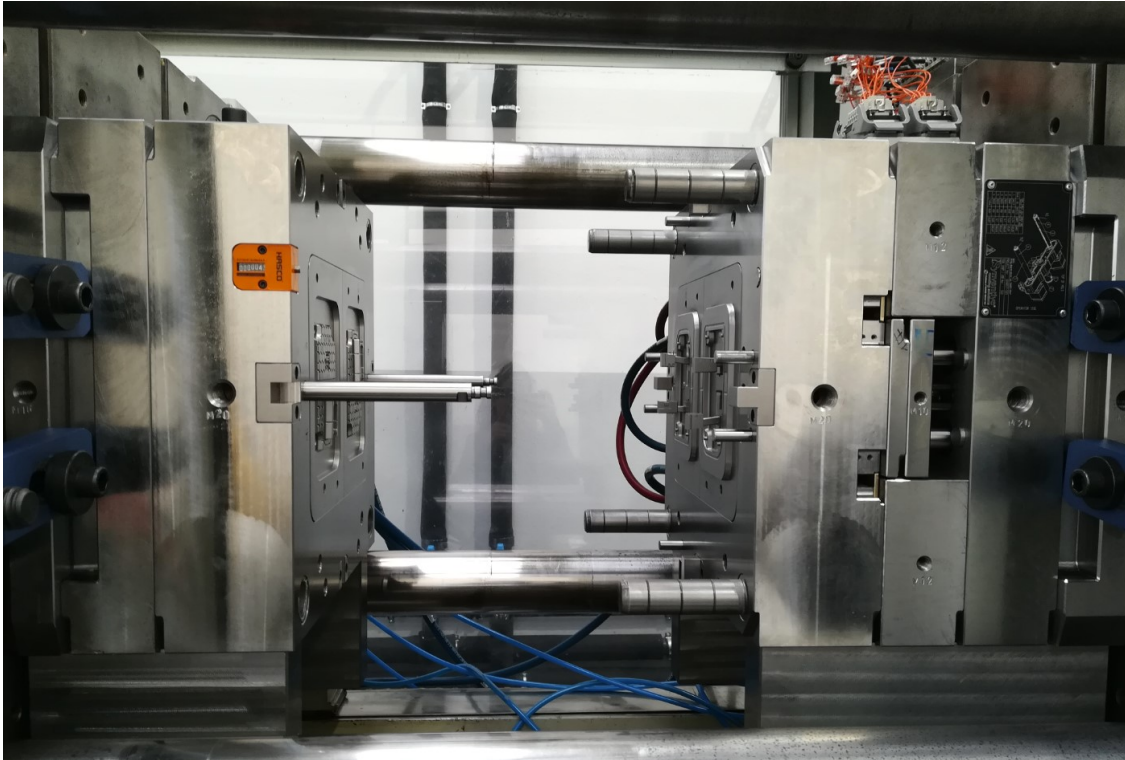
Molde na máquina de injeção prestes a realizar o teste (vista do lado do operador).
